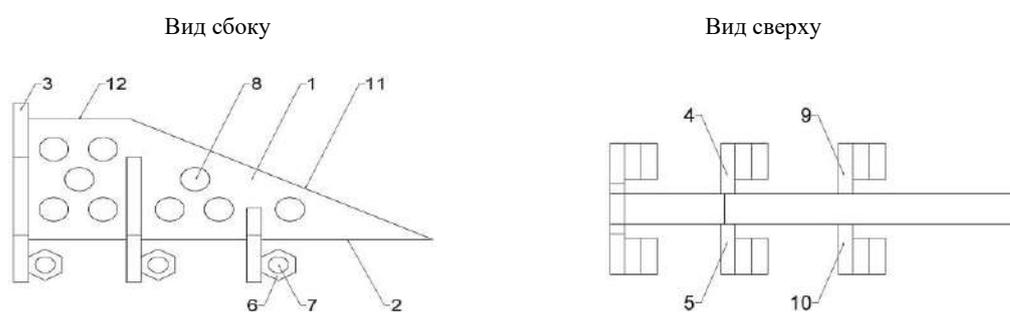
Устройство для поднятия колесной пары тепловоза:
